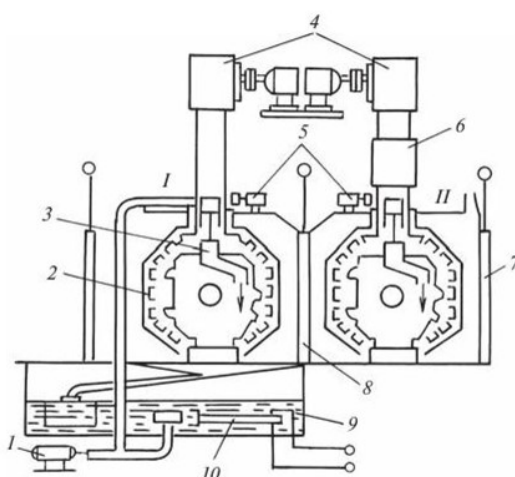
Двухкамерная машина для наружной обмывки и сушки тяговых двигателей перед разборкой
